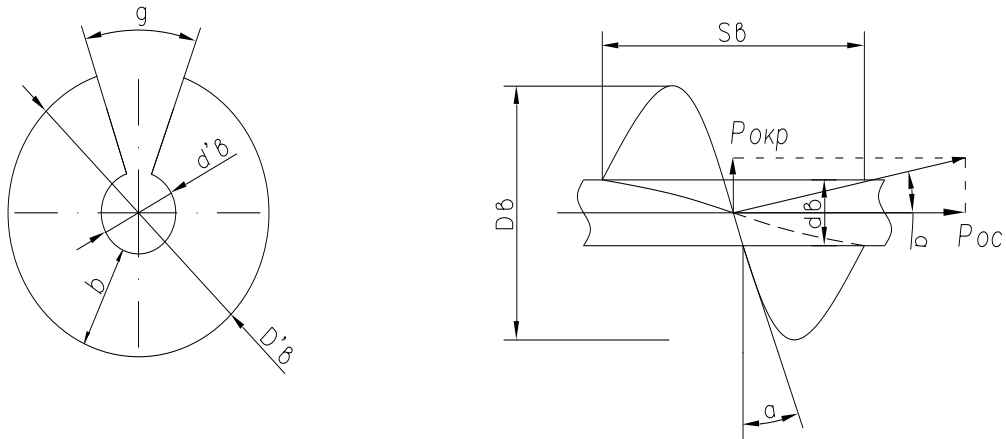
Схема до розрахунку розмірів заготовки шнека
